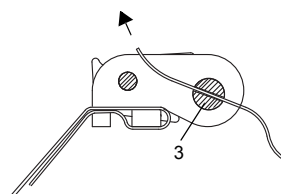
Cierre de trinquete con abrazadera de tensión
